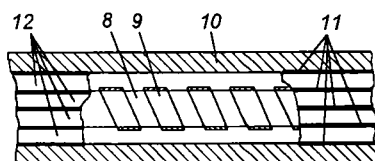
Конструкция ЧЭ на цилиндрической ЗС
